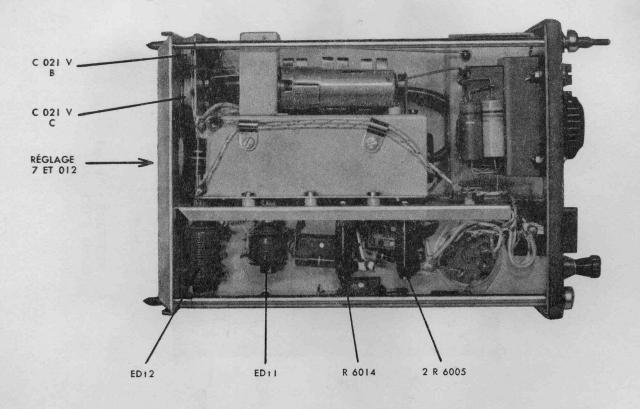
ÉMETTEUR VUE DE DESSOUS
